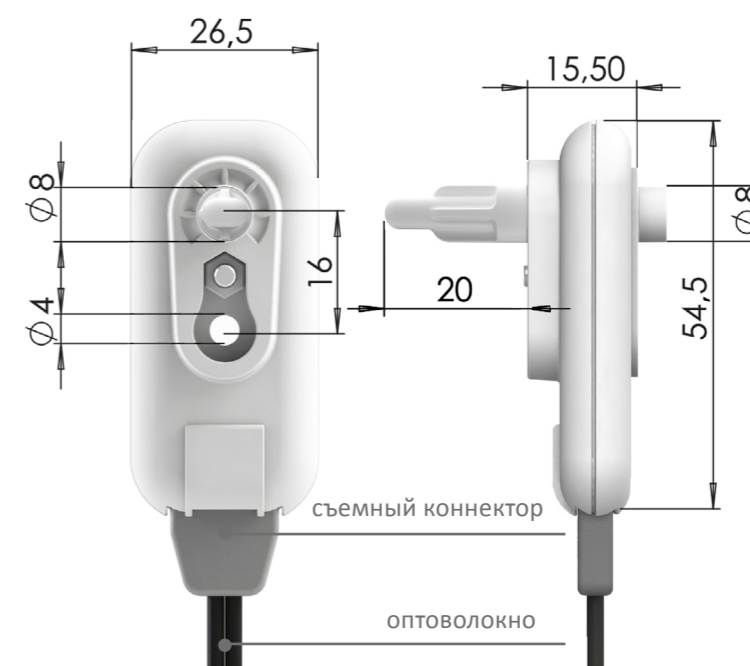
Внешний вид и габаритные размеры объектива ВОД
